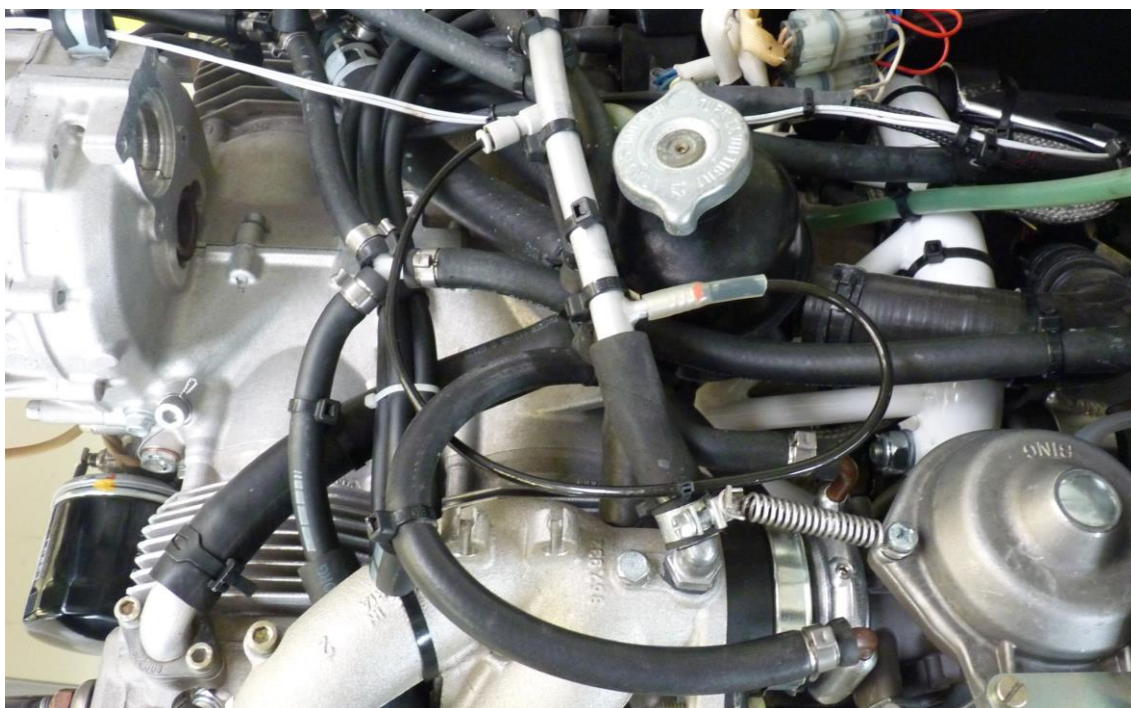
Schlauch für Ladedruck motorseitig angeschlossen
